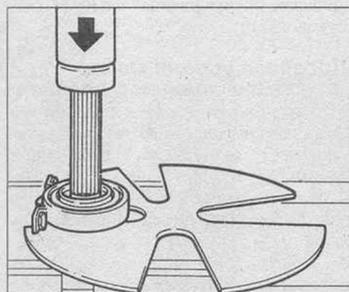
Выдавливание задней части карданного вала через центральный подшипник (Глава 3)
